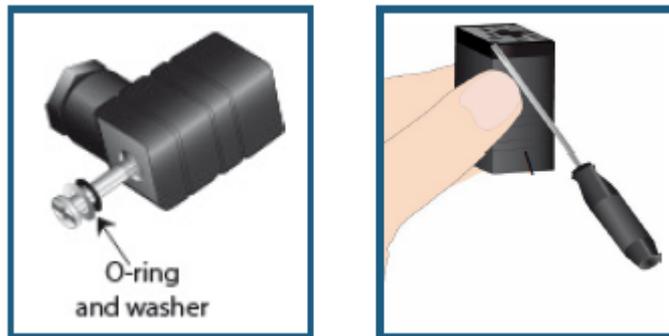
Entfernen des Steckverbinder-Klemmenblocks
